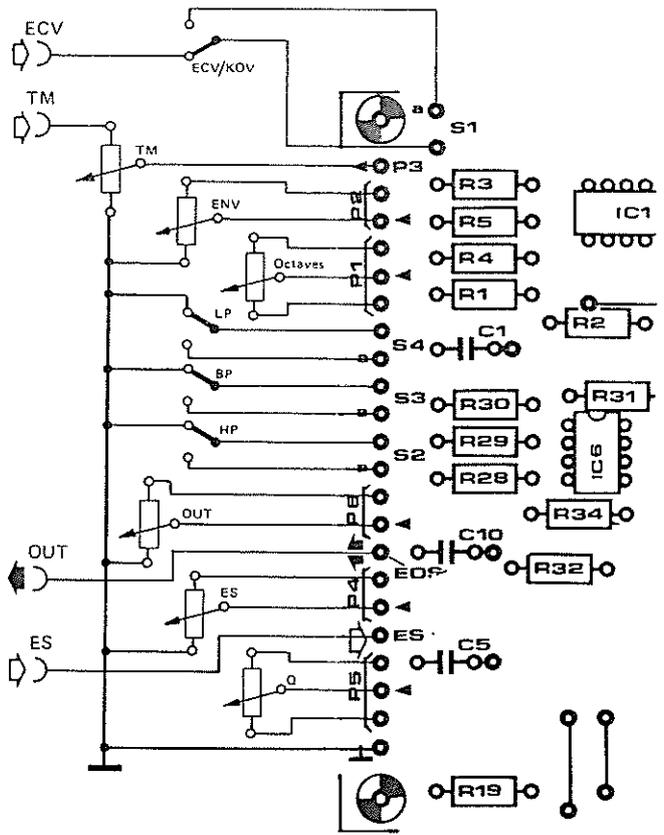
Platine mit Layout, Bestückungsplan und Stückliste des FORMANT-VCFs.
